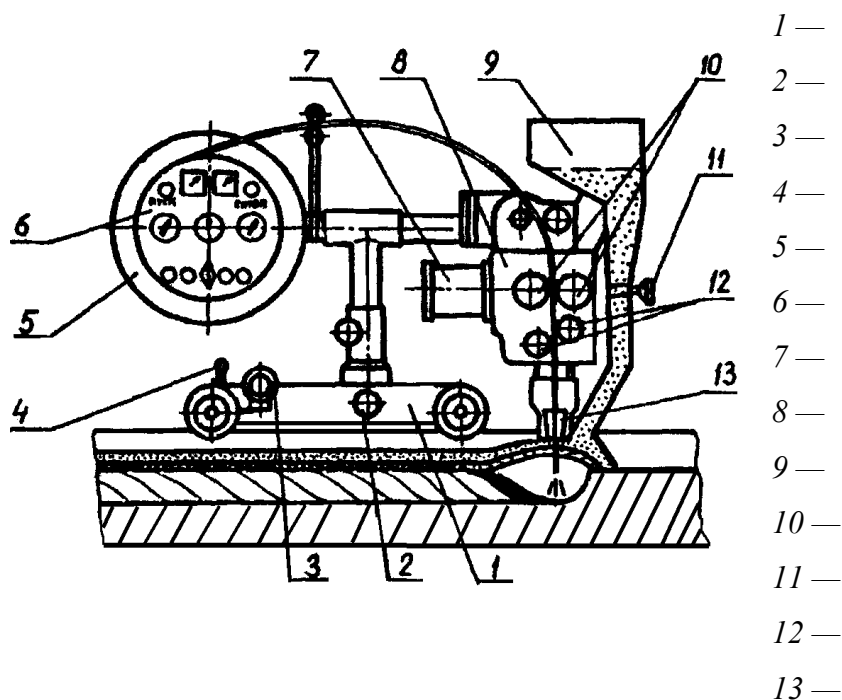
Схема устройства сварочного автомата АДС-1000
